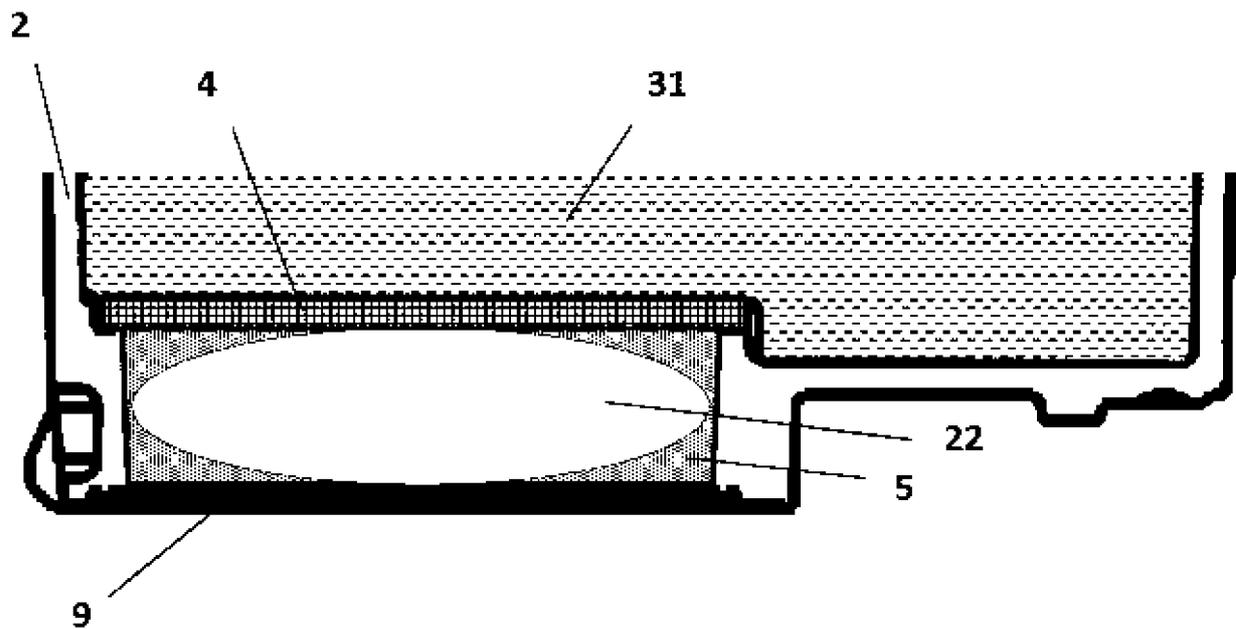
Поперечный разрез непрерывно перезаправляемого картриджа с печатающей головкой
